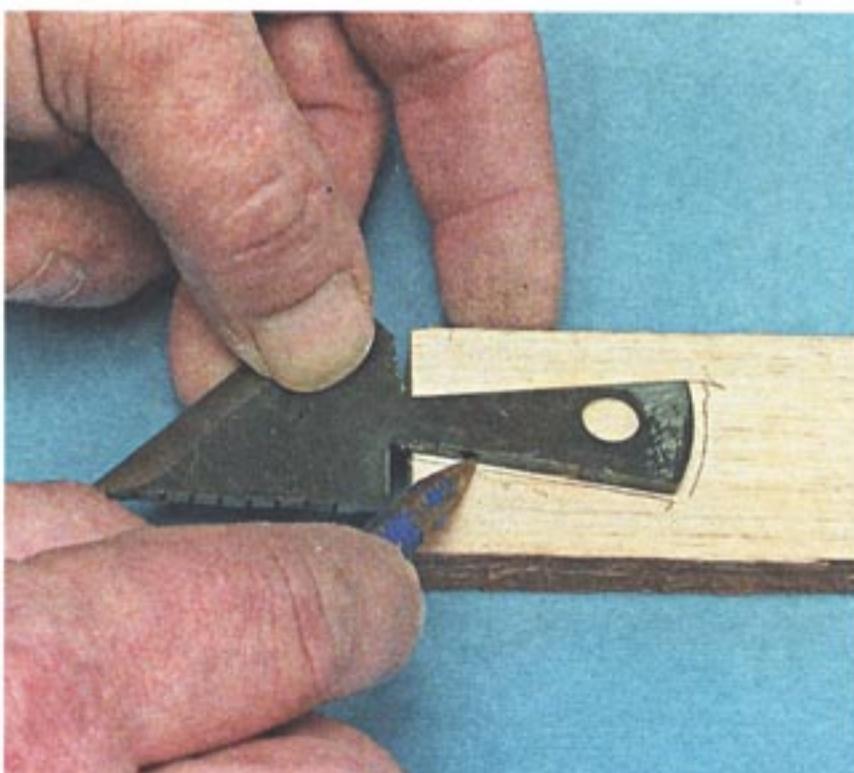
Разметка посадочного места под лезвие ножа-косяка на заготовке ручки
